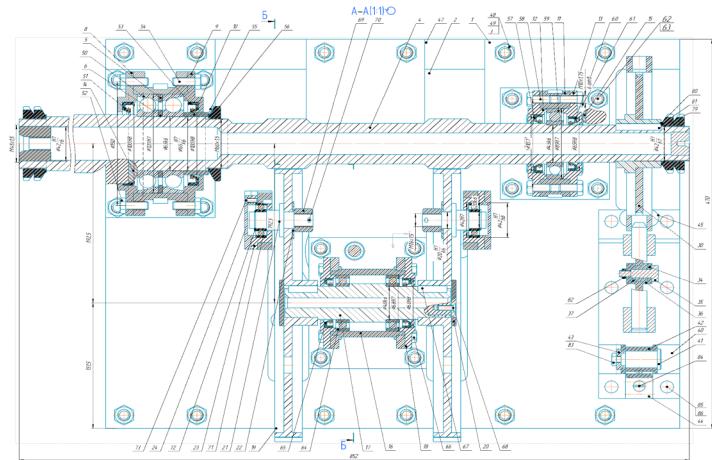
Сборочный чертеж силовой головки (разрез по горизонтали, по высоте оси вала ветрового колеса)
